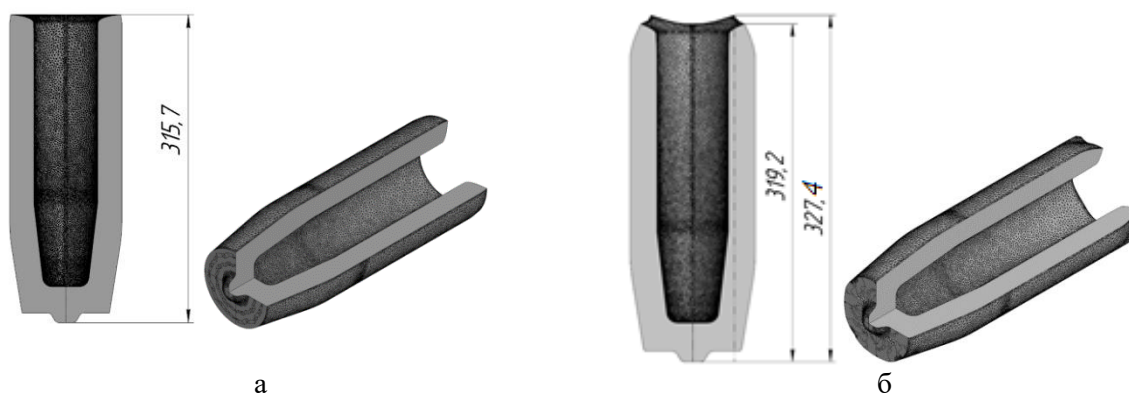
Кінцеві форми та розміри половин виробів та загальні вигляди з розрізом: а – після видавлювання заготовки круглого перерізу, б - після видавлювання заготовки квадратного перерізу
